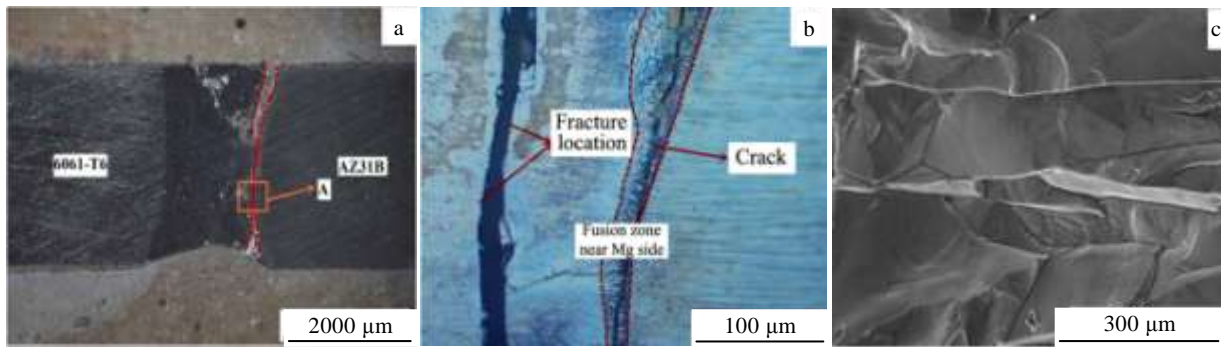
6061-T6/AZ31B 激光焊接接头断裂位置及断口形貌
